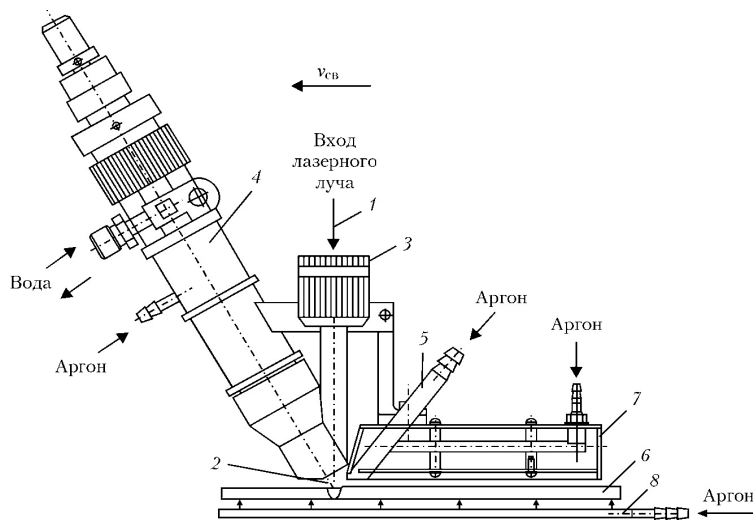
Схема гібридного лазерно-дугового зварювання: 1 – лазерний промінь; 2 – вольфрамовий електрод; 3 – плоскопаралельна пластина для вводу лазерного пучка; 4 – пальник для TIG-зварювання титану; 5 – пристрій для доп. подачі захисного газу; 6 – зразок зварювання; 7, 8 – захисний пристрій для захисту зони зварювання та остигаючого металу.
